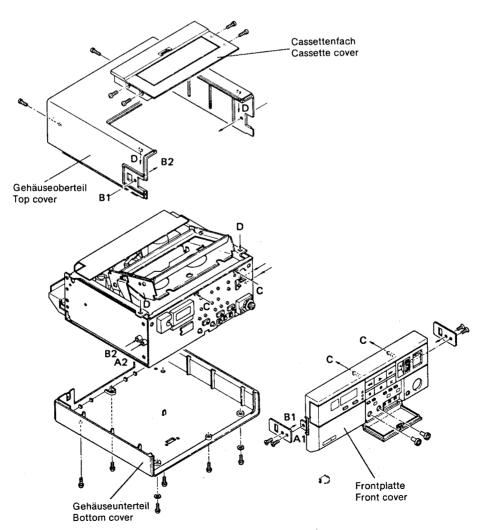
Gehäuseabdeckungen Fig. 1-1 External covers
